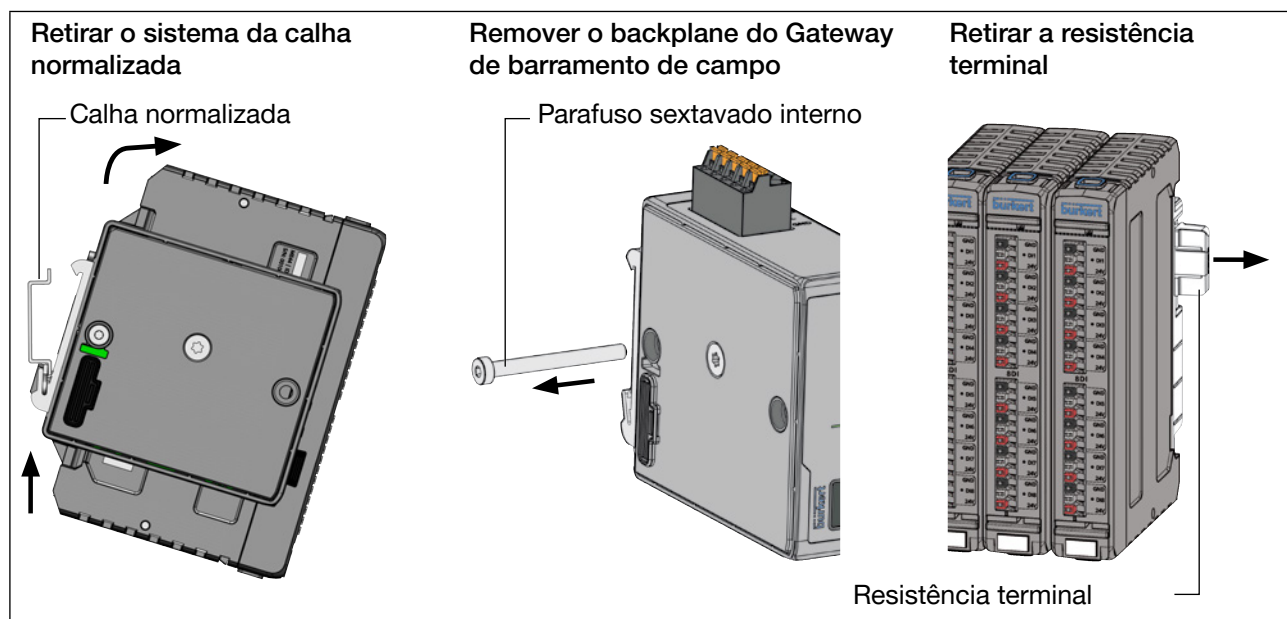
Desmontagem do backplane do Gateway de barramento de campo
